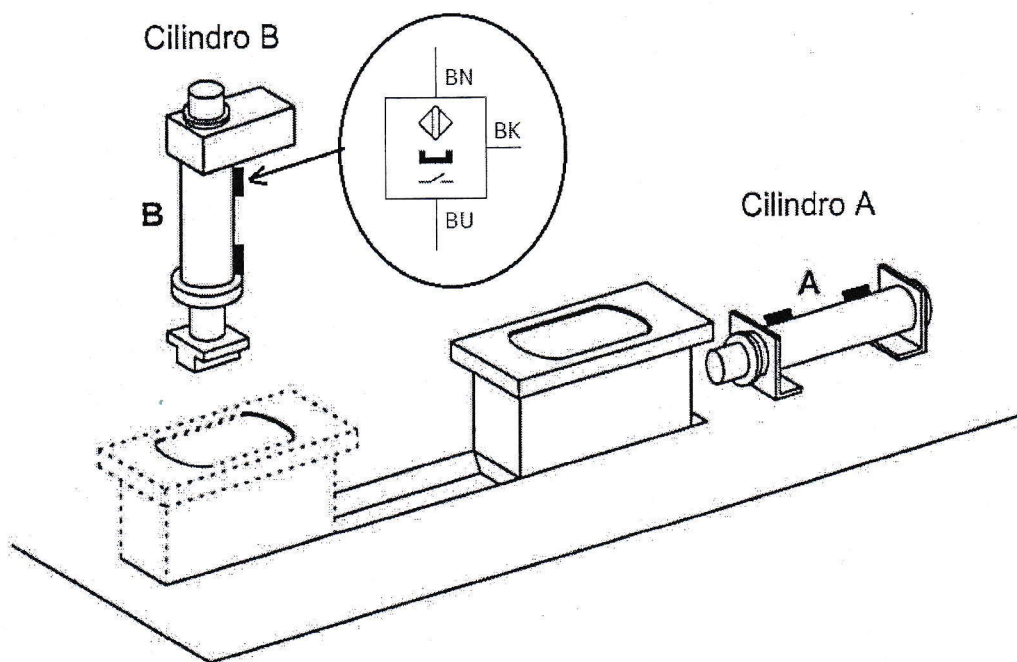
Croquis máquina electroneumática estampado de piezas
